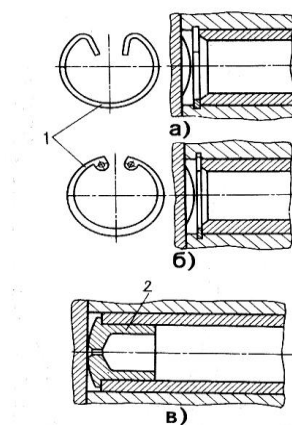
Схемы стопорения поршневых пальцев плавающего типа:
